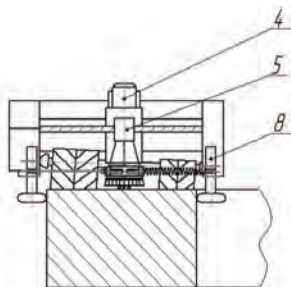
Передвижной станок для обработки торцов крупногабаритных деталей – вид сбоку
